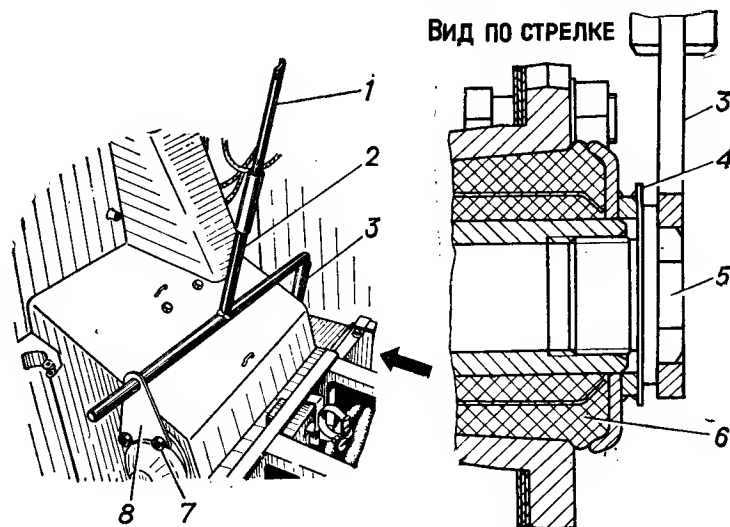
Подтяжка пробки задней резиновой втулки верхнего рычага подвески третьего правого колеса:
